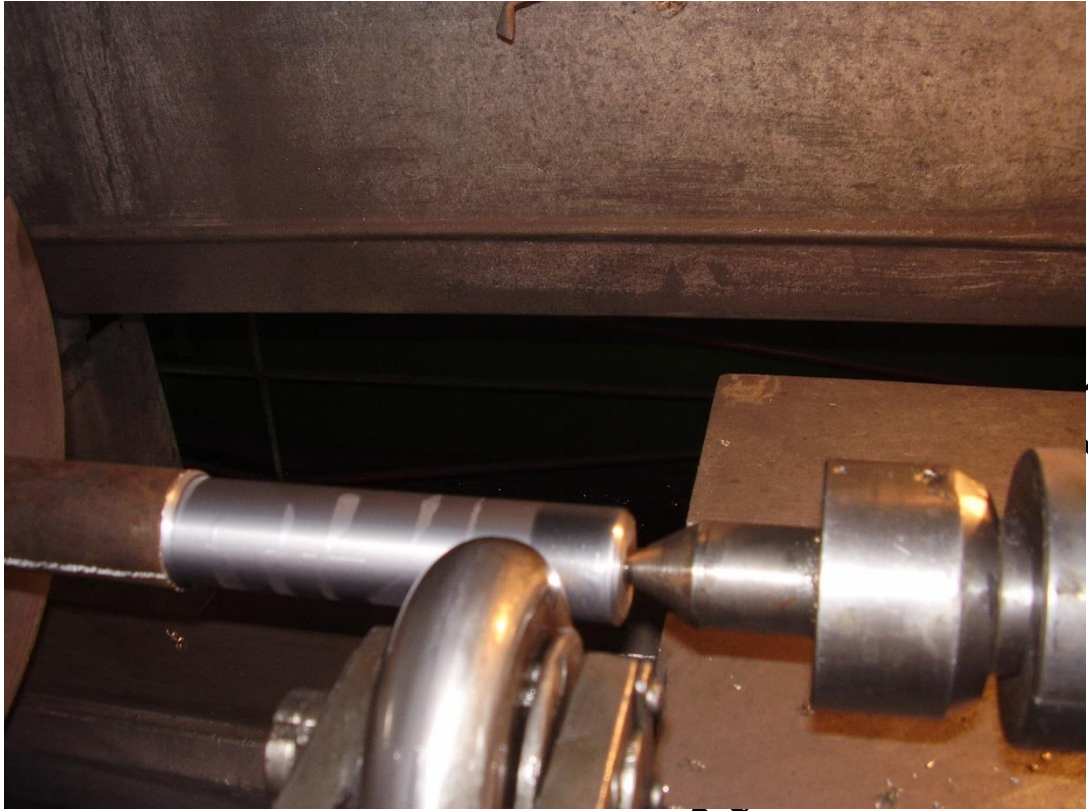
Обкатка вала із сталі 10X17H13M2Г з різними режимами обробки
